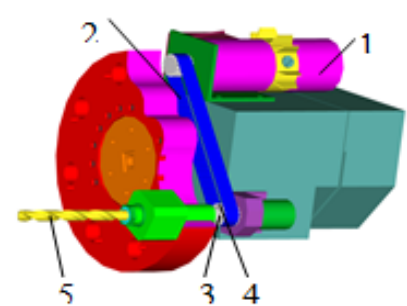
Схема шестипозиционной револьверной головки с вращающимся инструментом: 1 – приводной двигатель; 2 – зубчатая ременная передача; 3, 4 – полумуфты; 5 – инструмент
